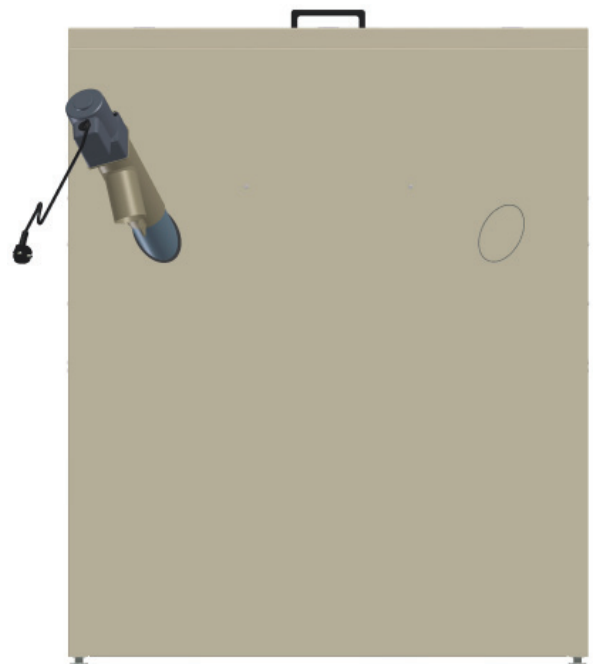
Assemblage Ensemble ZP600 + PP15/ PPL15.
